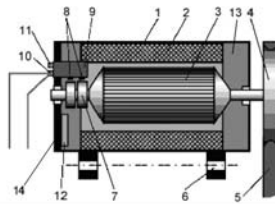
Генератор: 1 - корпус; 2 - обмотка статора; 3 - ротор; 4 - шків приводу генератора; 5 - ремінь; 6 - кріплення; 7 - контактні кільця; 8 - щітки; 9 - регулятор напруги; 10 - вихід, 11 - випрямляч
